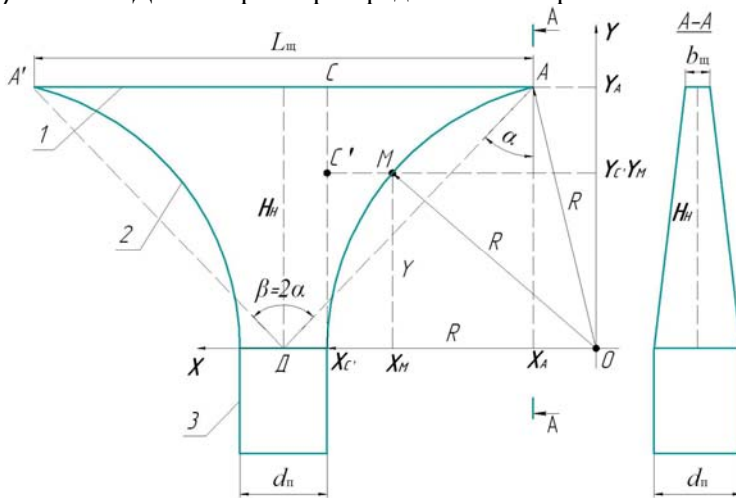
Розрахункова схема конструктивних параметрів насадка 1 – всмоктувальна щілина насадка; 2 – бокова твірна стінка корпусу насадка; 3 – патрубок насадка
